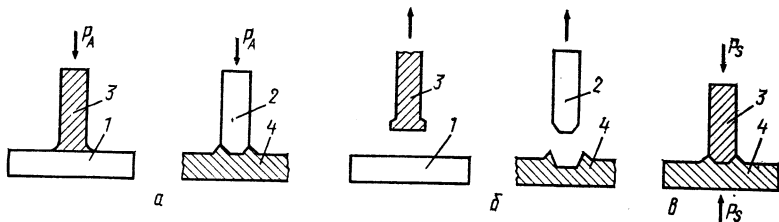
Принцип сварки панелей и фасонных деталей в выточку: а — подогрев свариваемых деталей; б — отвод нагретого инструмента; в — состыковка (сварка); 1, 2 — нагретые инструменты; 3, 4 — свариваемые детали
